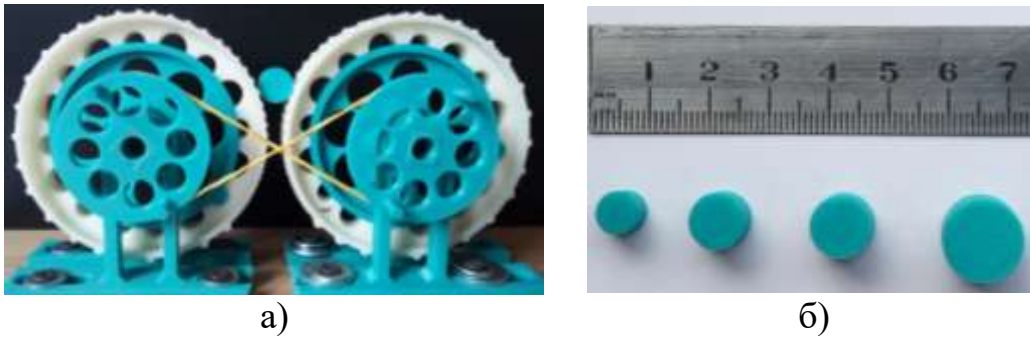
Установка (а) для определения условий захвата материала (б) рифлеными валками
